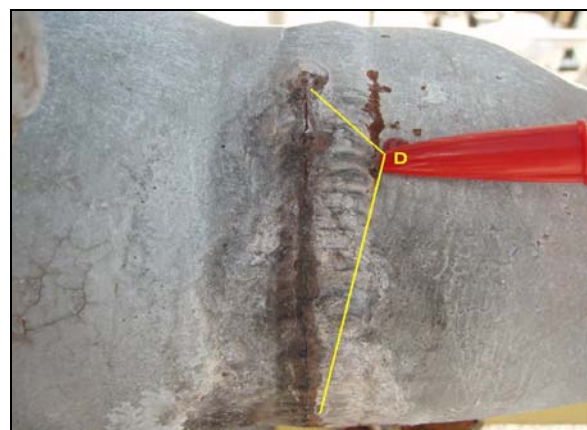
Trinca longitudinal ao cordão de solda.
